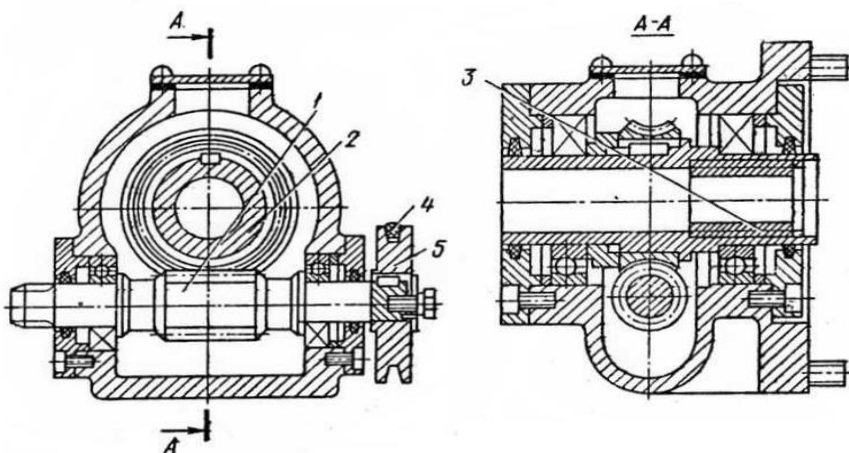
Редуктор вертикальной подачи станка мод. 3Е711В
